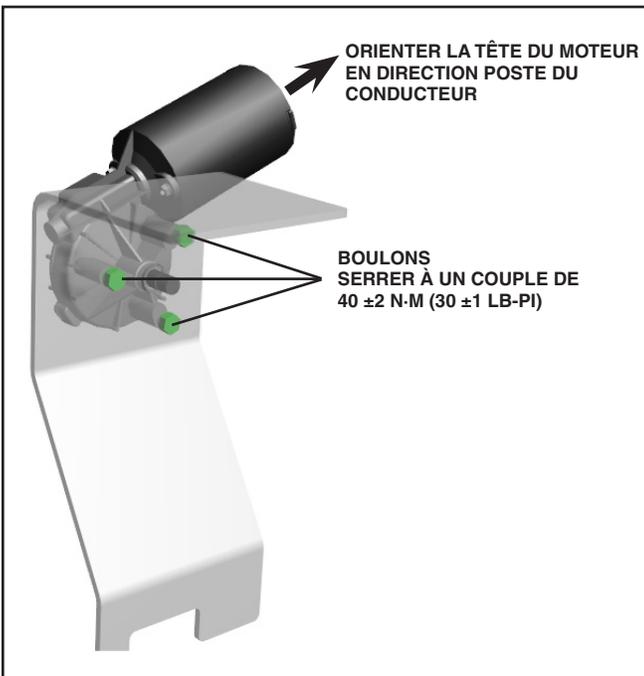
Installation du moteur des essuie-glaces - vue de derrière le support
